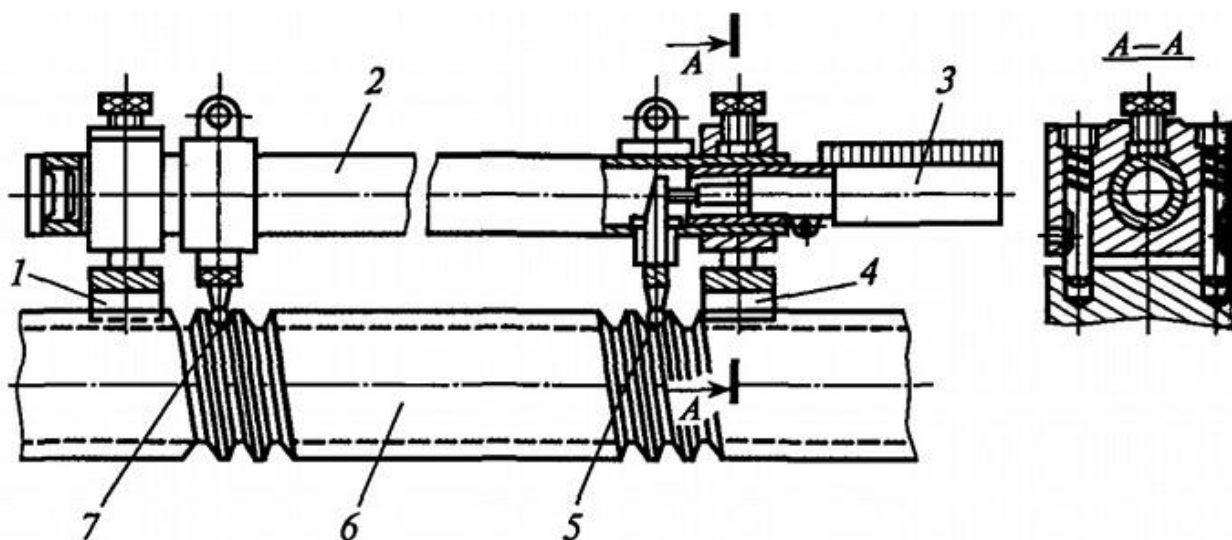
Приспособление для контроля точности шага ходового винта:
